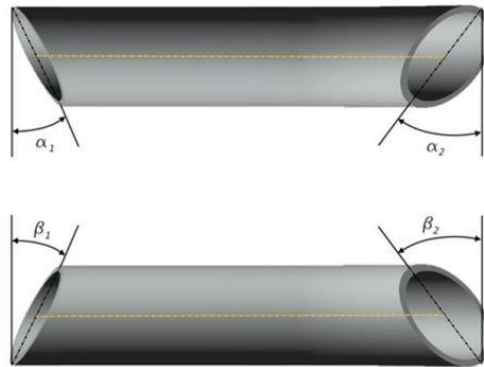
Патрубок круглого перерізу прямої форми з обробленими торцями:
